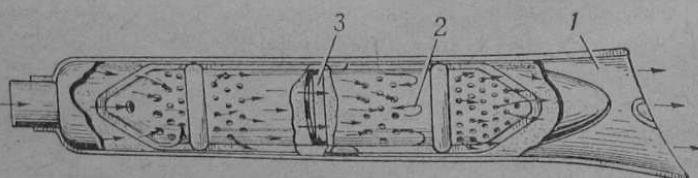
Глушитель неразборного типа мотоцикла М-72:
